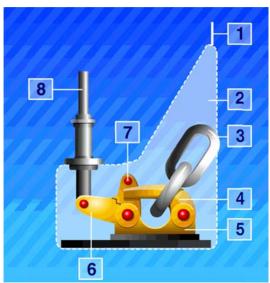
Крепление коренного конца якорной цепи: 1 – переборка цепного ящика; 2 – ниша; 3 – якорная цепь; 4 – откидной гак; 5 – обух; 6 – рычаг;
